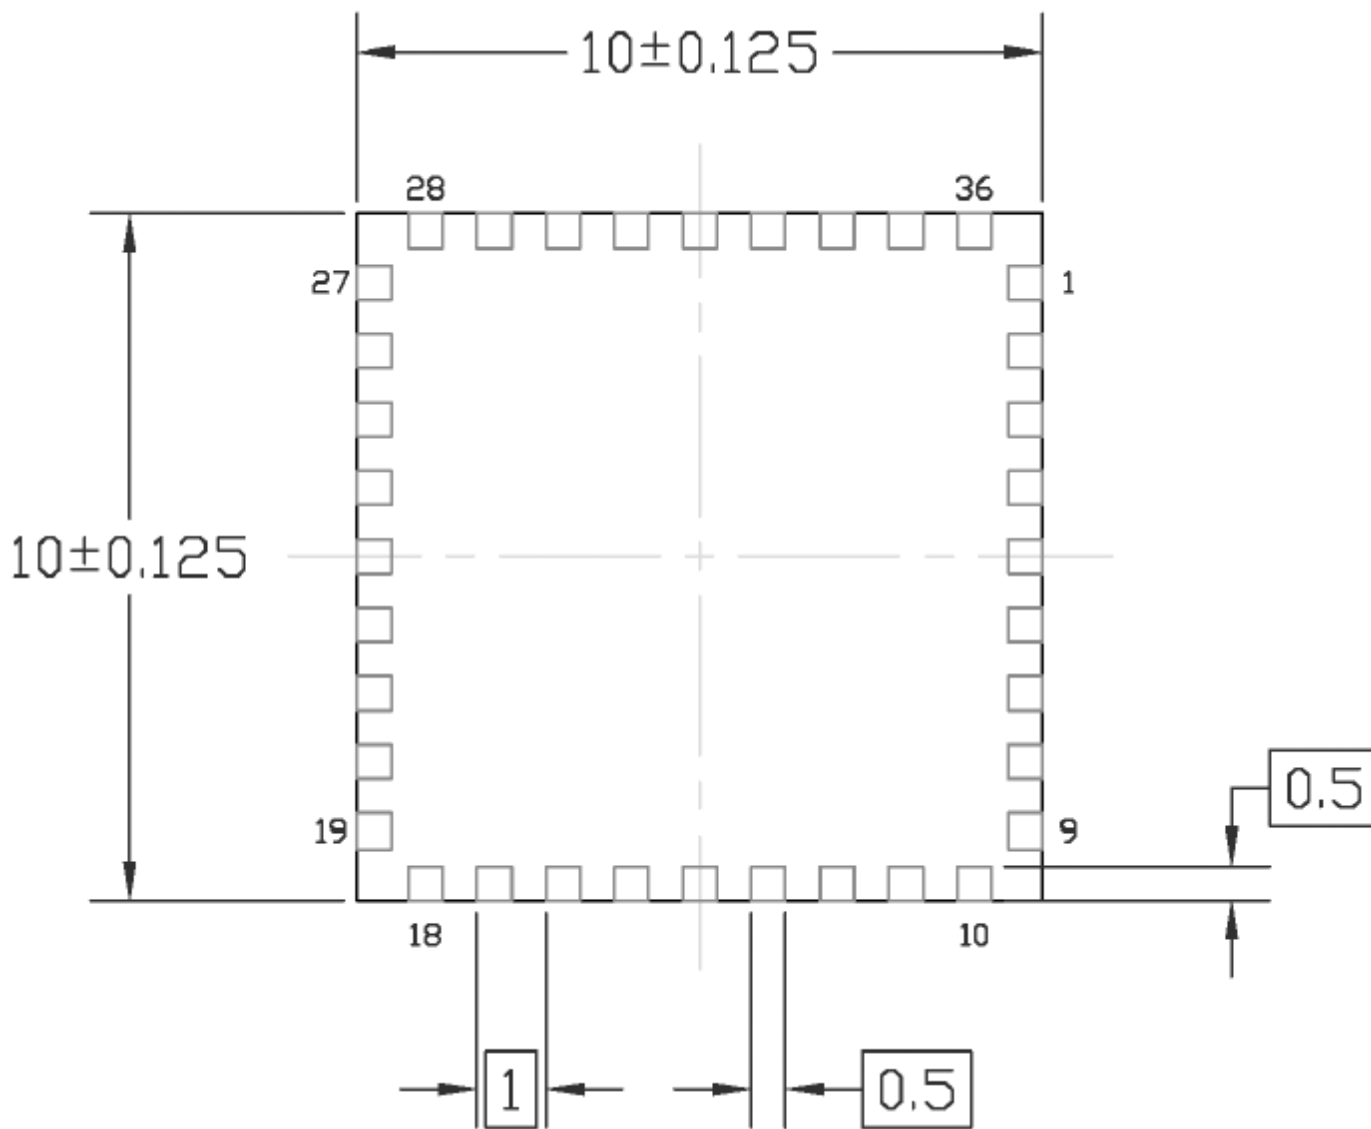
PCB Footprint recomendado (en mm) – Vista desde arriba.
